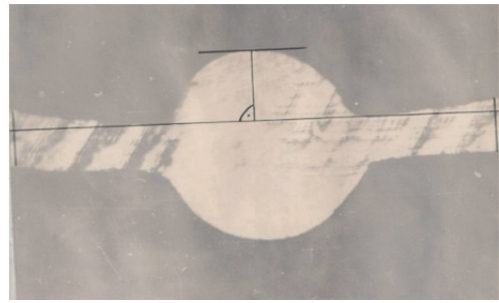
Поперечное сечение контрольной поковки после изготовления 500 деталей, образец № 5
